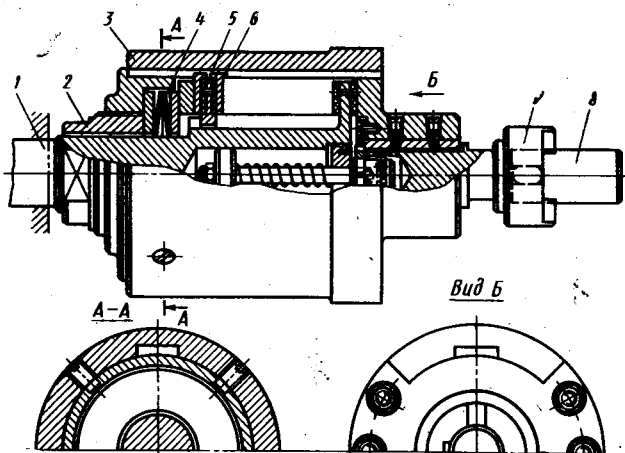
Фрикционный патрон для нарезки резьбы М120
